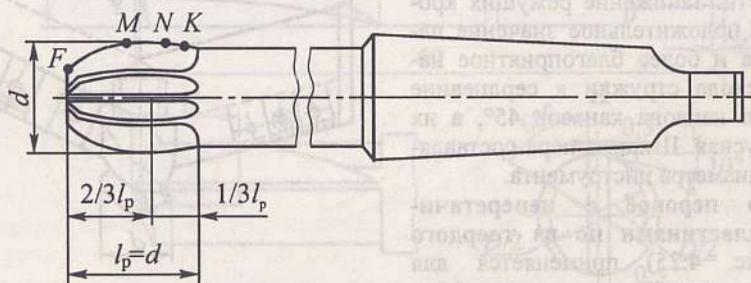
Развертка с эллипсоидной формой рабочей части
